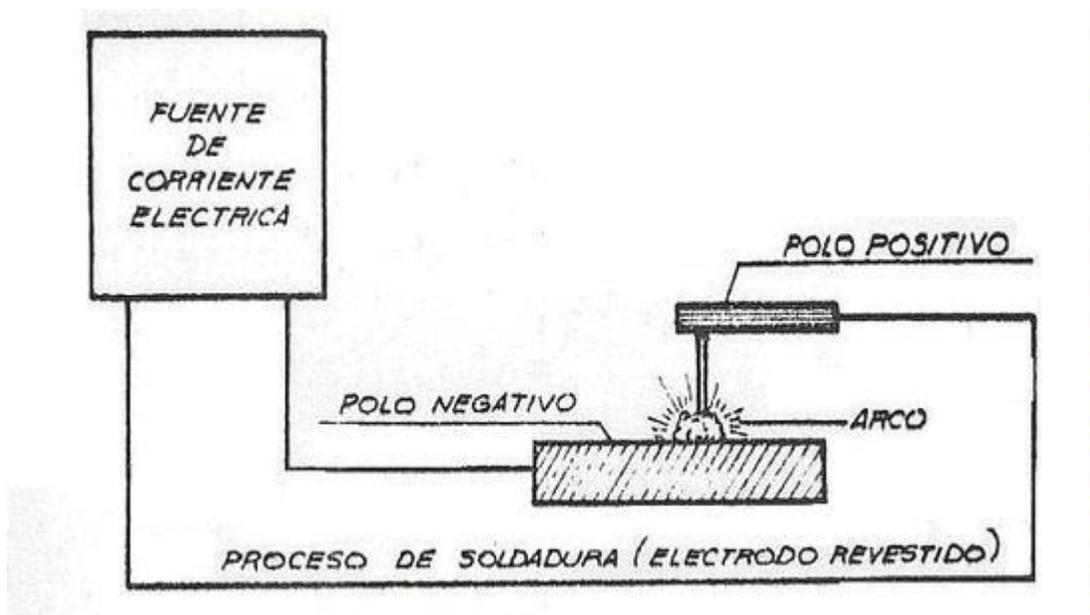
Partes de la soldadura por arco eléctrico.
